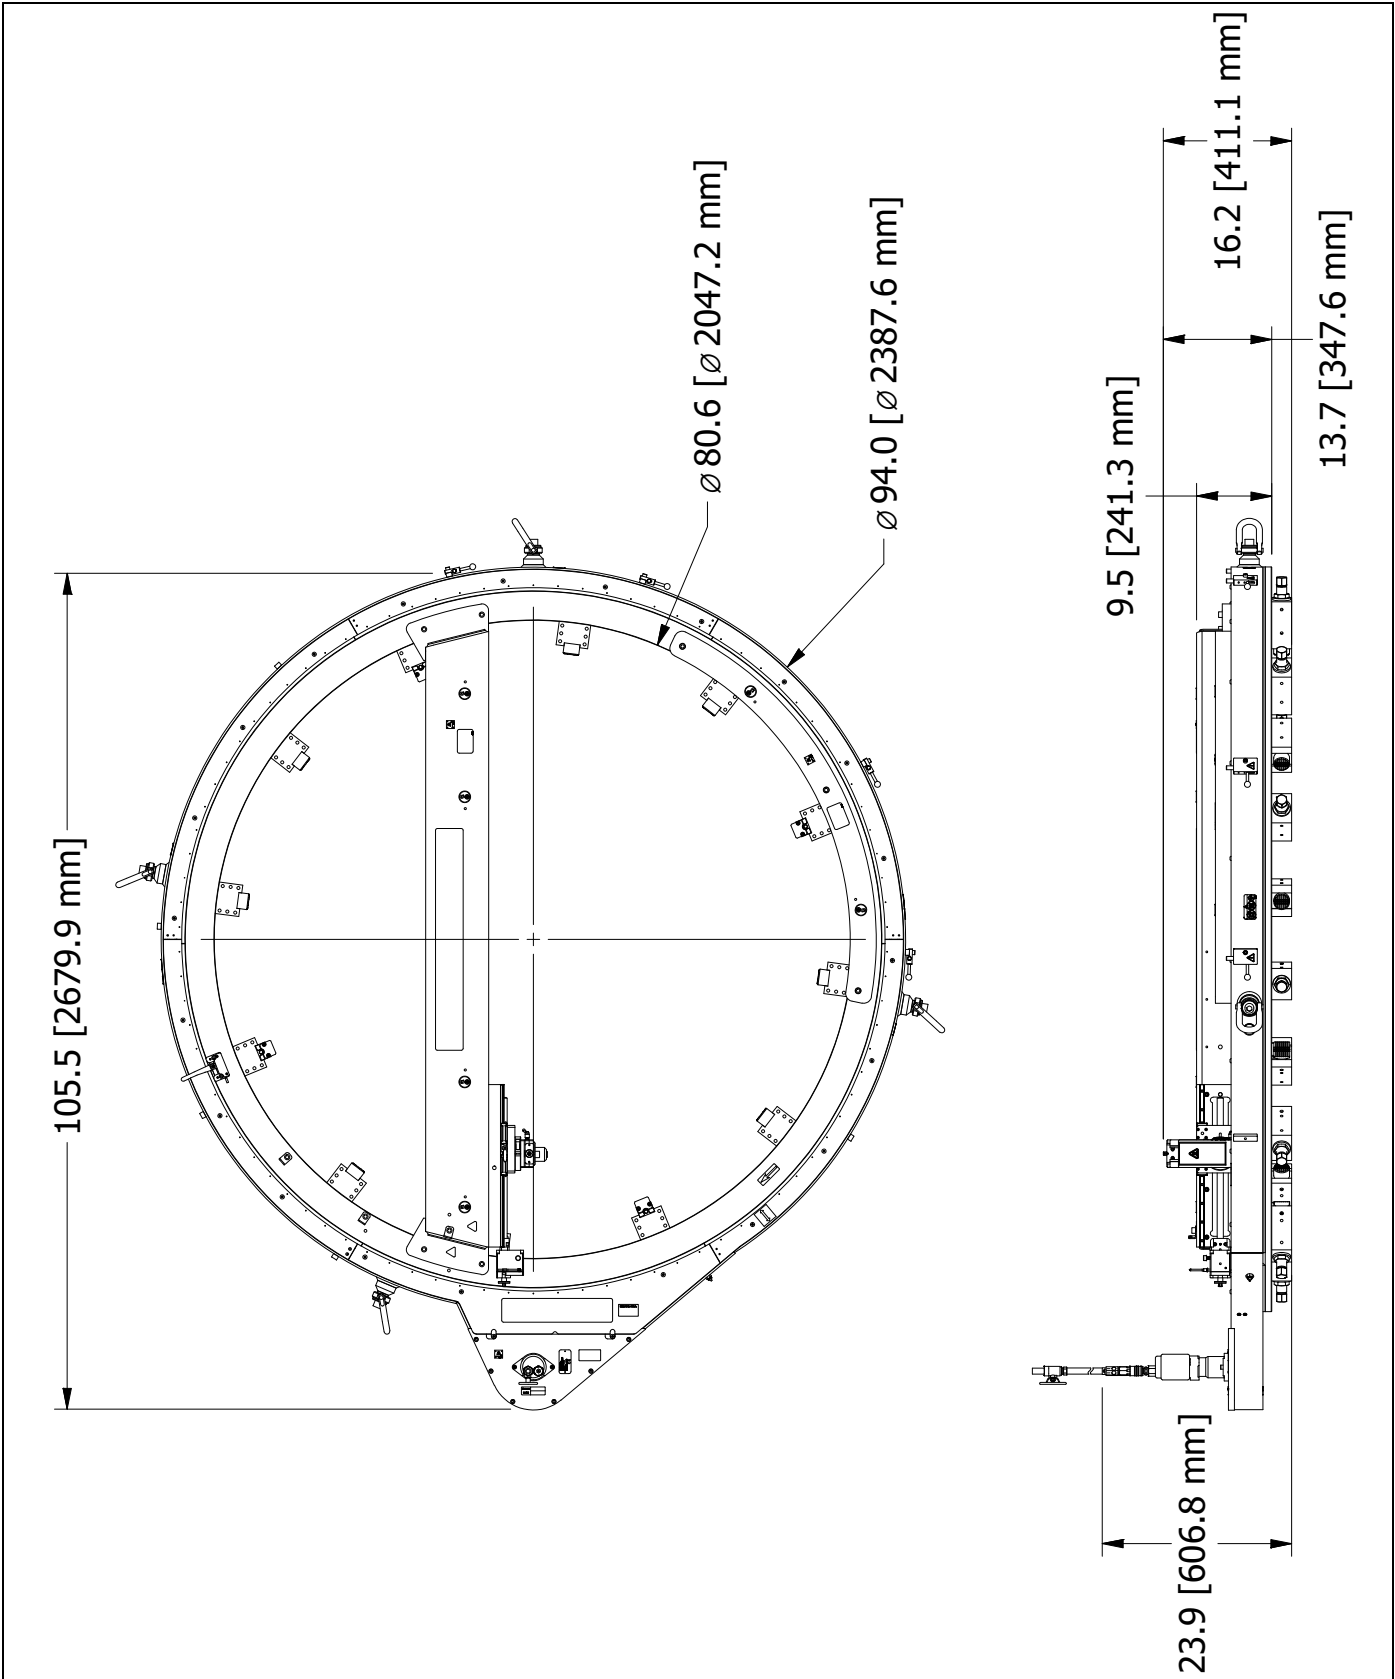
DIMENSIONES DE ODF80 SPEED FACER (N/P 94770)
